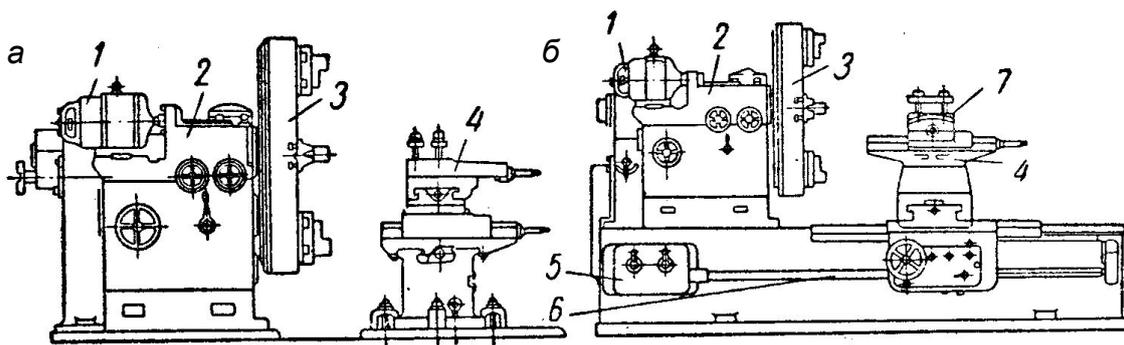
Основные типы токарно-лобовых станков: а – с суппортами; б – с суппортами, установленными на станине; 1 – электродвигатель; 2 – коробка скоростей; 3 – планшайба; 4 – суппорт; 5 – коробка подач; 6 – ходовой вал; 7 – резцедержатель
